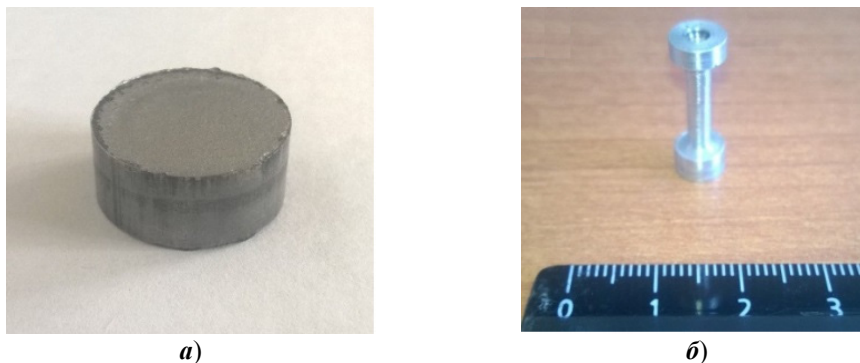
Образцы после ИПС: *а* – образец Ø20×10 мм; *б* – образец для испытания на растяжение, изготовленный из цилиндра Ø10×20 мм
